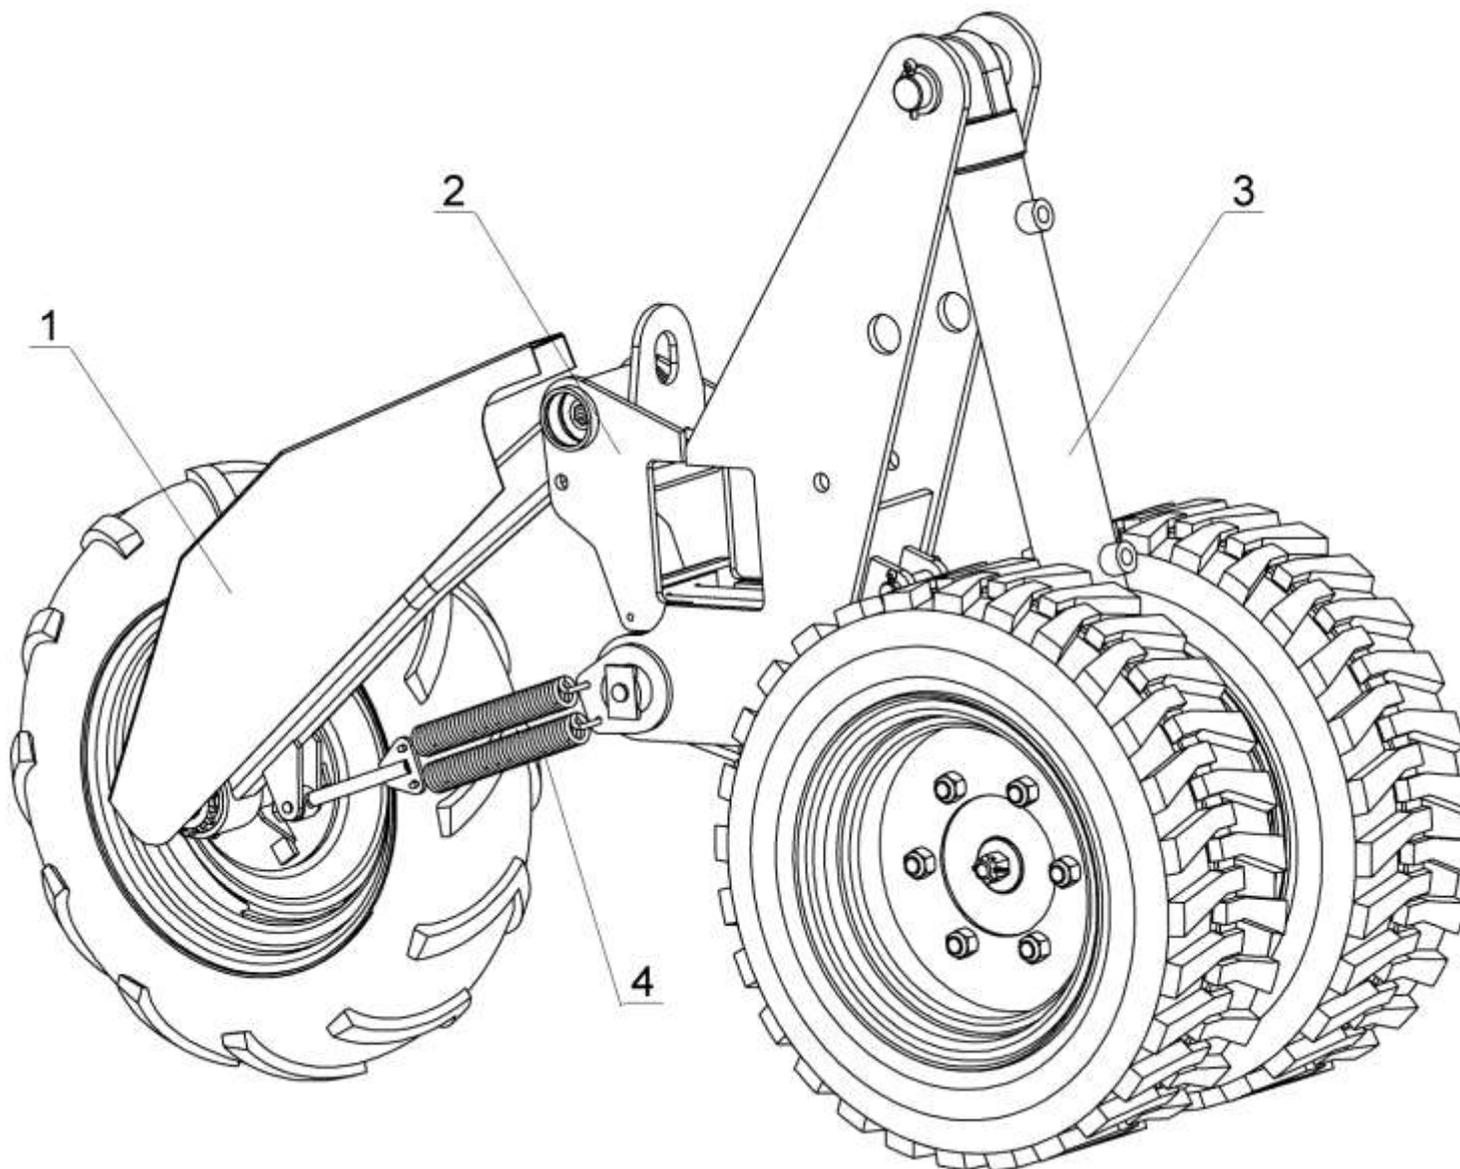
Колесо опорно-приводное СУС 00.4970А
